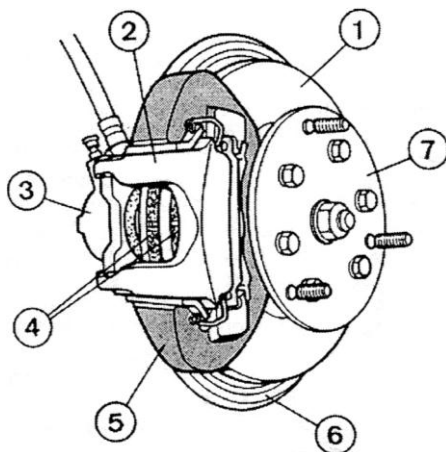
Конструктивная схема дискового тормозного механизма с подвижным суппортом:
